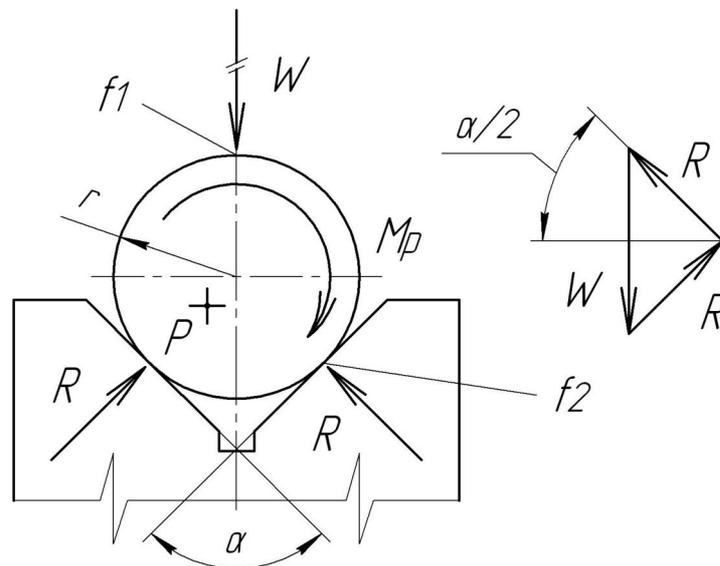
Схема сил действующих на заготовку при ее установке в призму
